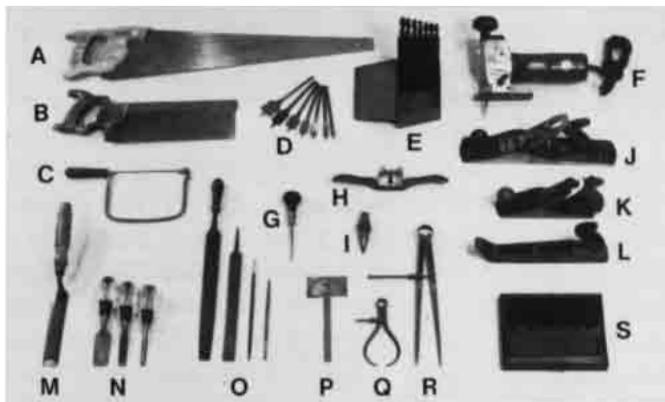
Erweiterter Werkzeugsatz: (A) Fuchsschwanz; (B) Fuchsschwanz für Gehrungslade; (C) Bügelsäge; (D) Zentrumsbohrer, großer Satz; (E) Spiralbohrer, großer Satz; (F) elektrische Stichsäge; (G) Ahle; (H) Ziehklängen-Hobel; (I) Lot; (J) Schrupphobel; (K) Schlichthobel; (L) Raspelhobel; (M) Stecheisen, gekröpft; (N) Stecheisen-Sortiment; (O) Feilen- und Raspel-Sortiment; (P) Winkelmesser; (Q) Taster; (R) Zirkel; (S) Abziehstein.
